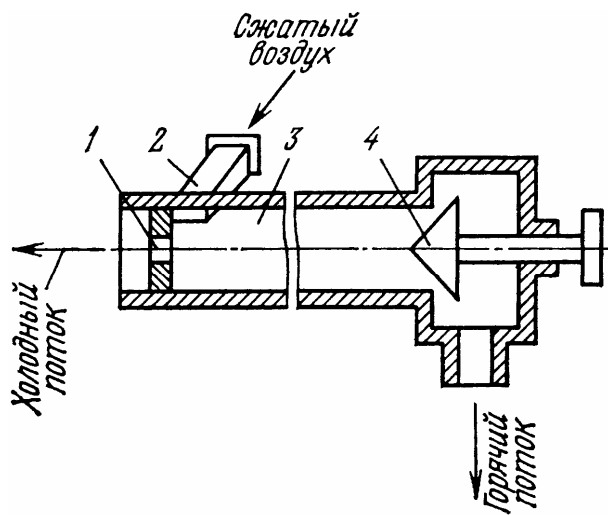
Вихровий охолоджувач: 1 – діафрагма; 2 – тангенціальне введення; 3 – суміжний відрізок труби; 4 – дросельний вентиль
